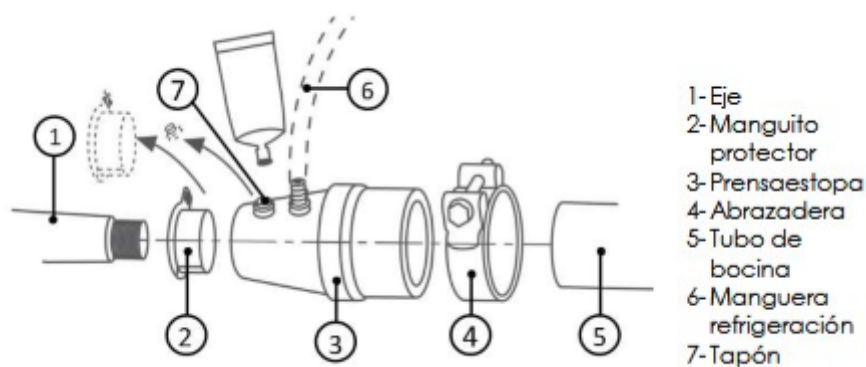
Bocina húmeda – Fuente: Solé Diesel
